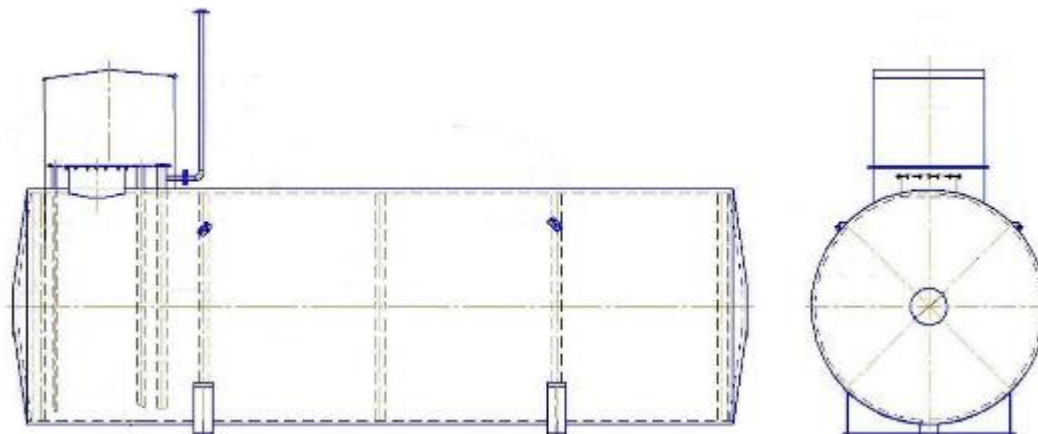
Эскиз общего вида резервуаров РГС-50
